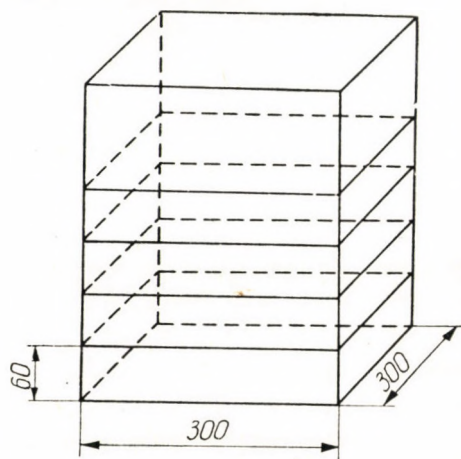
Разрез болванки сплава альпака на пластины для прокатки
